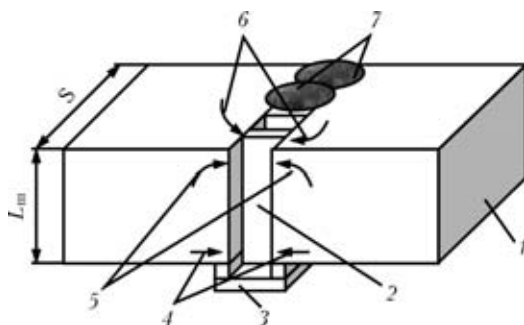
Схема ожидаемых деформаций деталей при МЭШС: 1 — свариваемая деталь образца; 2 — формирующая пере-
